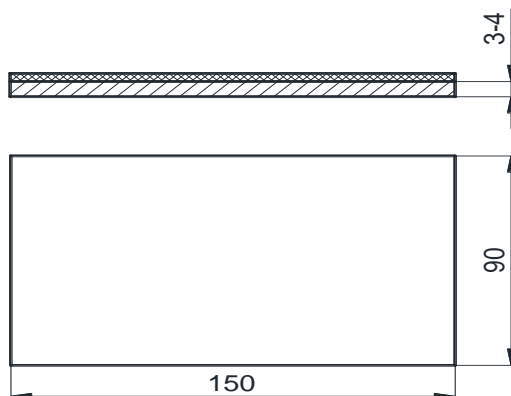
Схема образца – пластины из стали 20 с защитным покрытием
